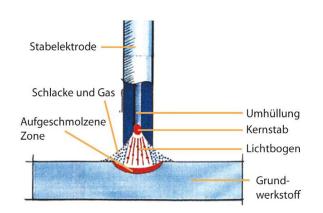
Funktionsprinzip Lichtbogenhandschweißen
